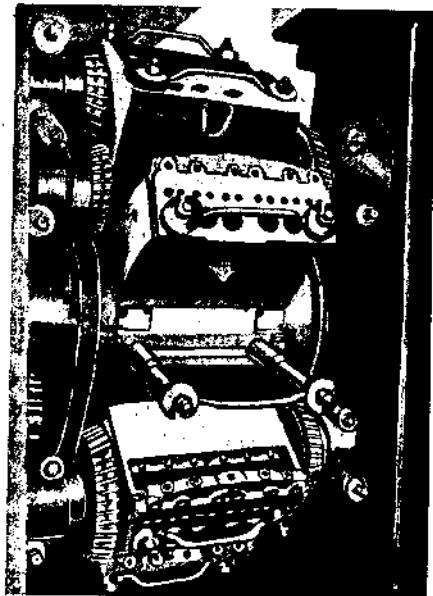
Расположение фрезеров на барабанном станке фирмы Ньютон.
